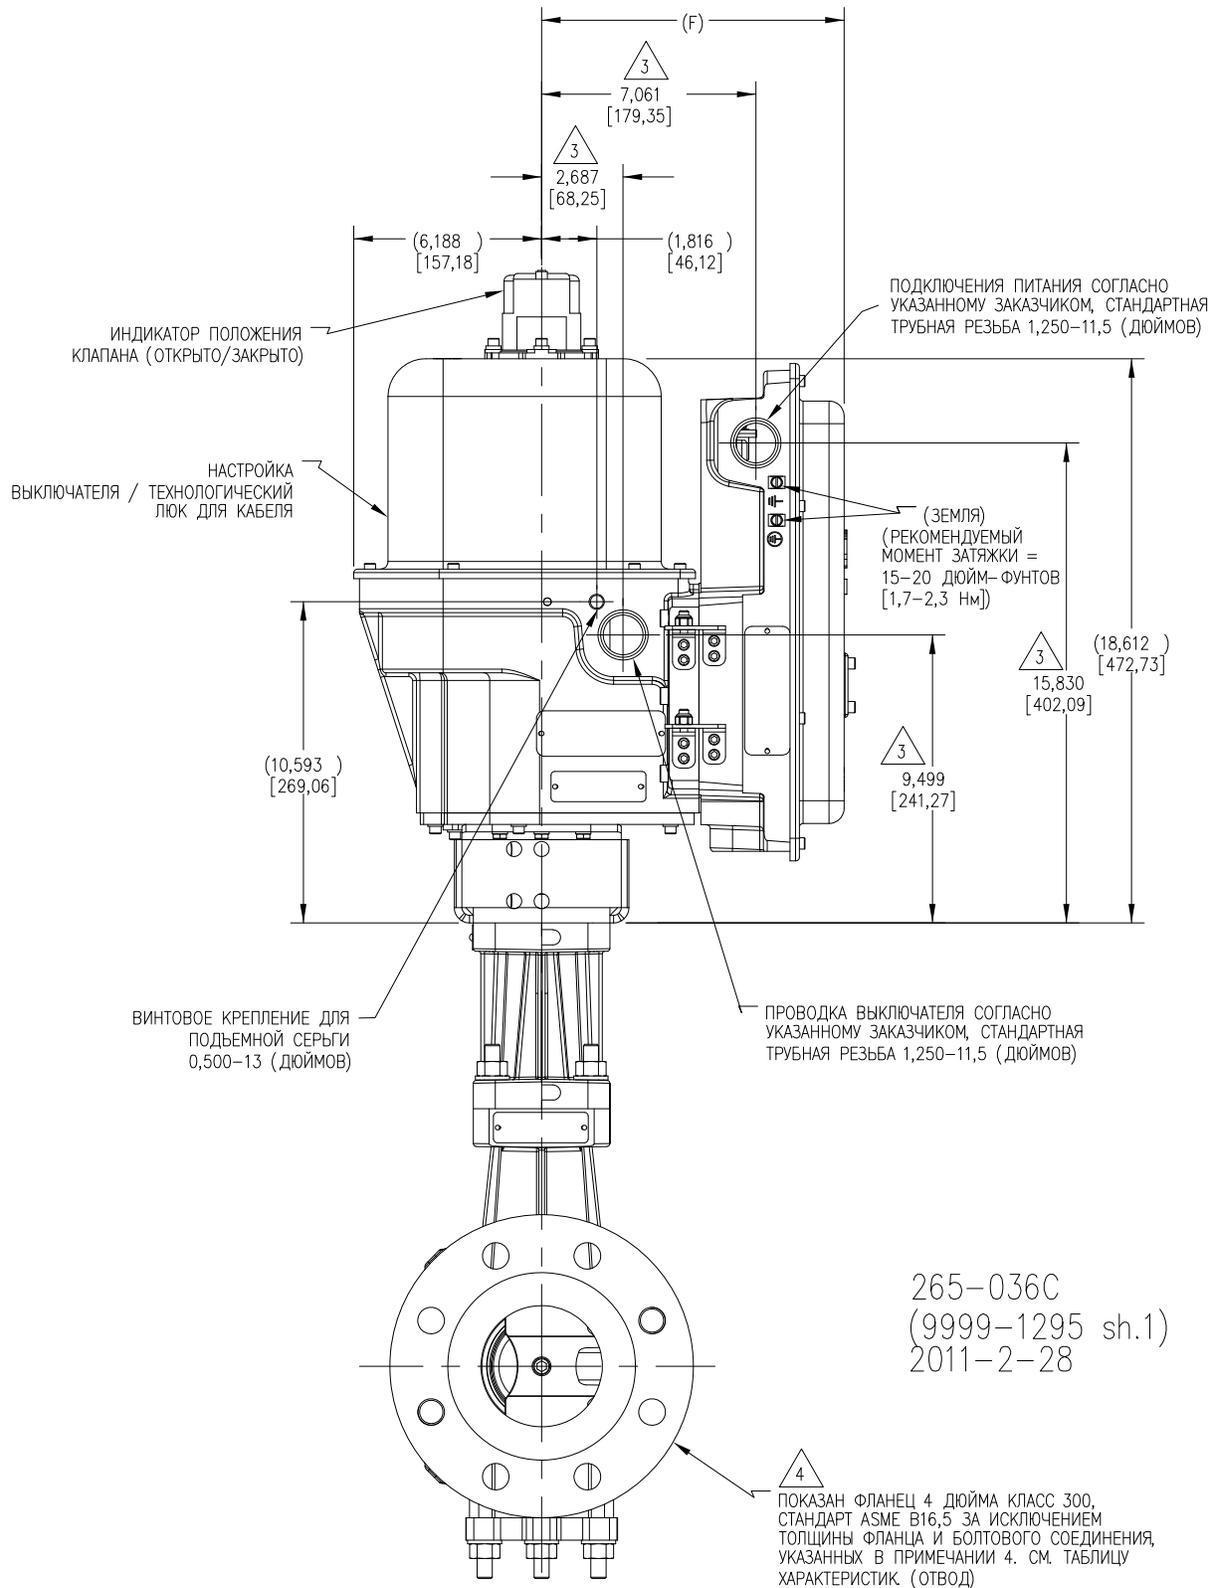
е. Габаритно-присоединительный чертеж RVP-200
